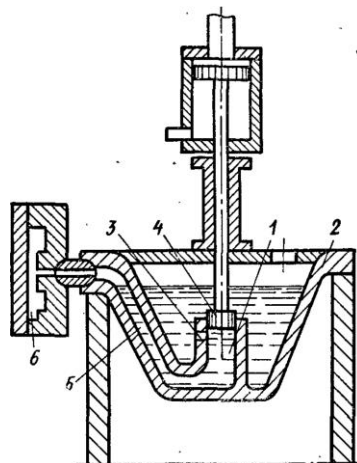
Схема машины для литья под давлением с горячей камерой прессования
